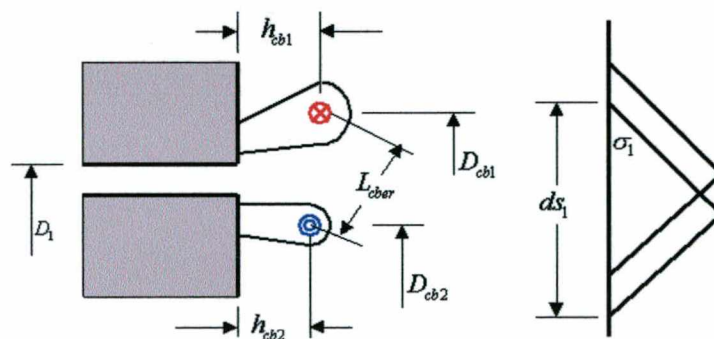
Configuração Geométrica das Cabeças de Bobinas do Estator e do Rotor
